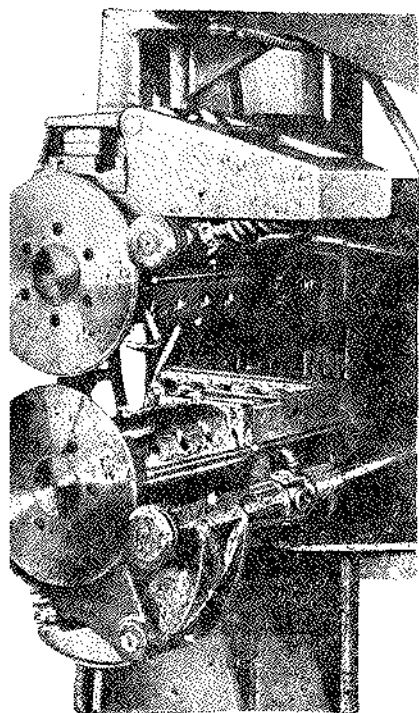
Схема роликовой сварочной машины на 300 кВА.
